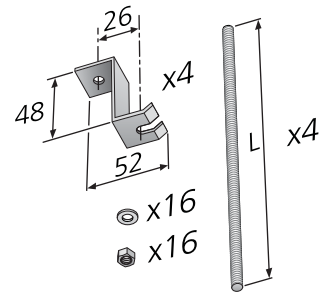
Montagestück SYST MS-1, Deckenbefestigung Gewindestange
